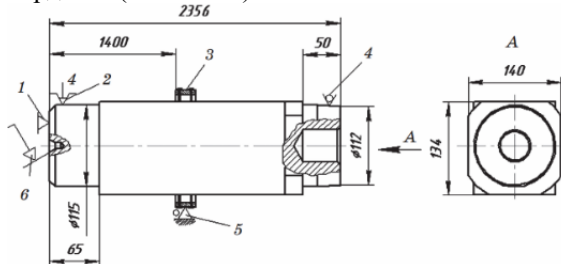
Схема встановлення заготовки: 1 – упор; 2 – патрон 4-х кулачковий; 3 – втулка під люнет; 4 – центруюча втулка маслоприймача; 5 – люнет роликівий 3-х кулачковий; 6 – центр пристосування
